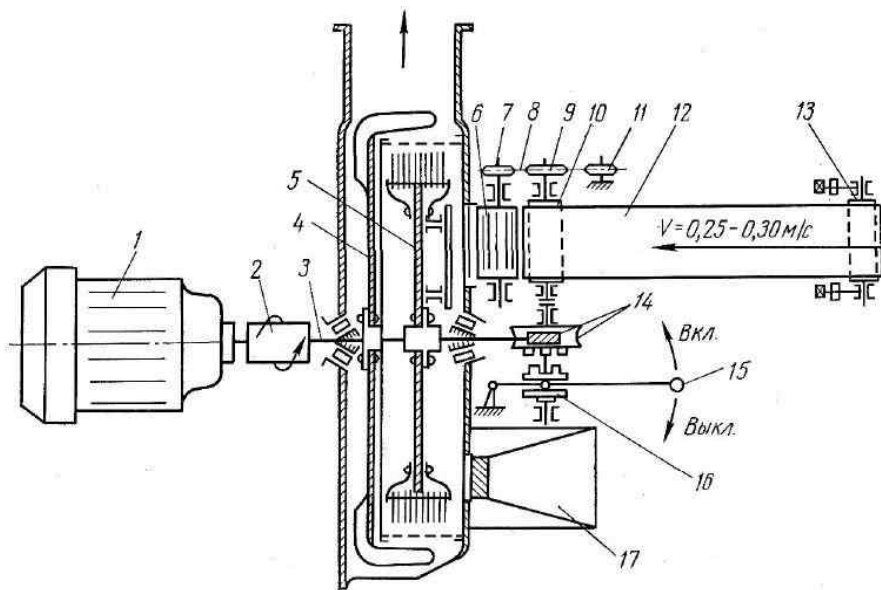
Кинематическая схема универсальной дробилки кормов ДКУ-М:
